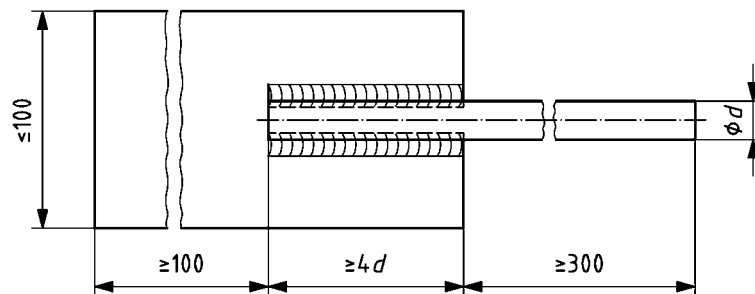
Probe für Zugversuch für andere Verbindungen (beidseitige Flankenkehlnähte)
